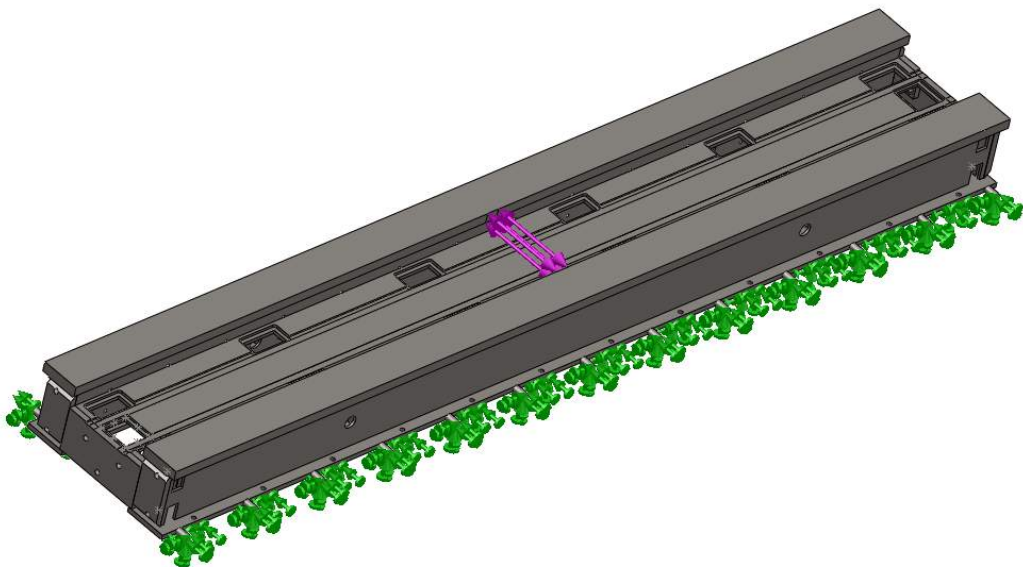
Твердотільна модель зварної станини під супорт
